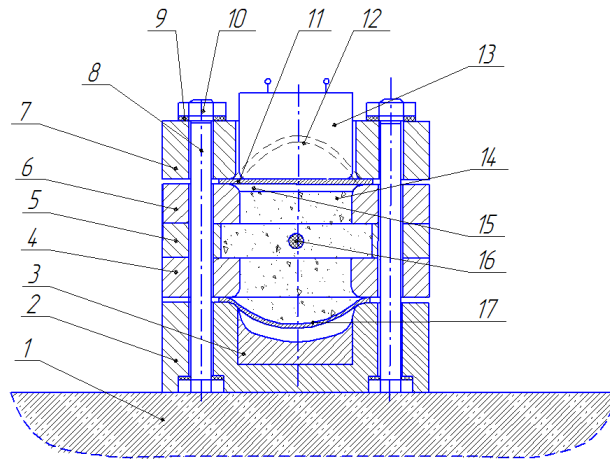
Схема пристрою для штампування листових деталей імпульсними джерелами енергії
